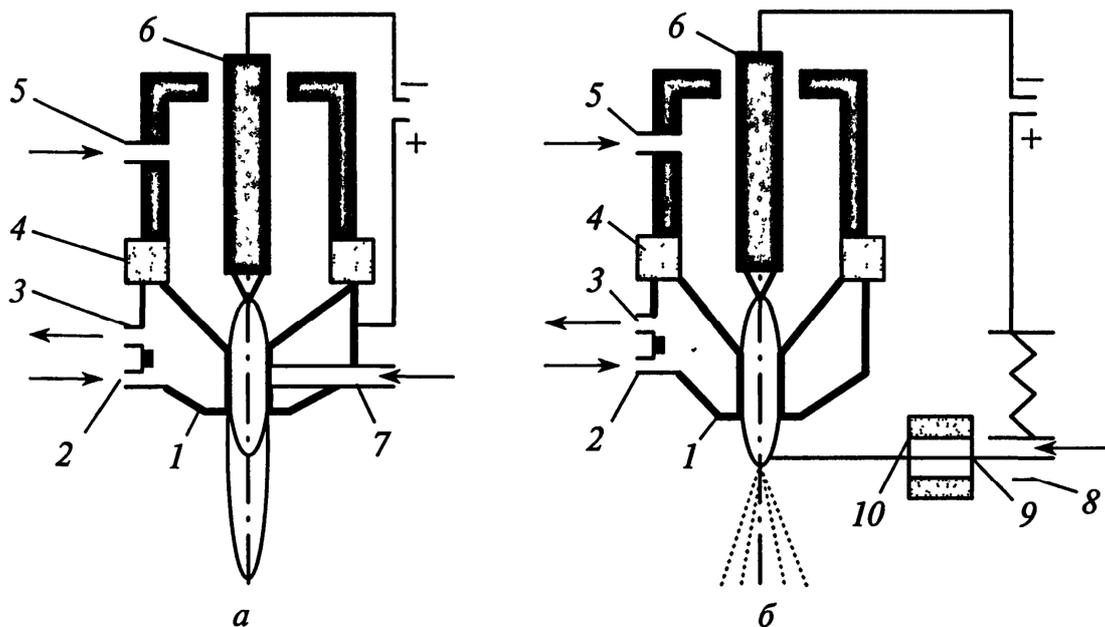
Схема плазмотрона: *а* – для работы на порошках; *б* – для работы на проволоке; 1 – сопло плазменной струи (анод); 2, 3 – подвод и отвод охлаждающей воды; 4 – изолирующее кольцо; 5 – подвод плазмообразующего газа; 6 – вольфрамовый электрод (катод); 7 – подача напыляемого порошка; 8 – контактное устройство для проволоки; 9 – напыляемая проволока (анод); 10 – направляющая трубка для проволоки
